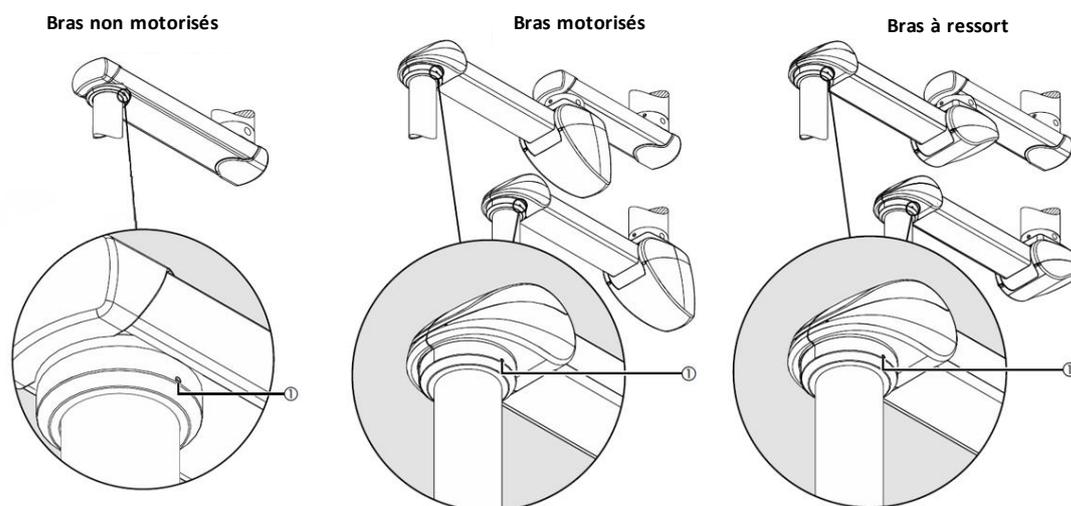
Réglage du frein à friction sur le tube de descente avec palier
